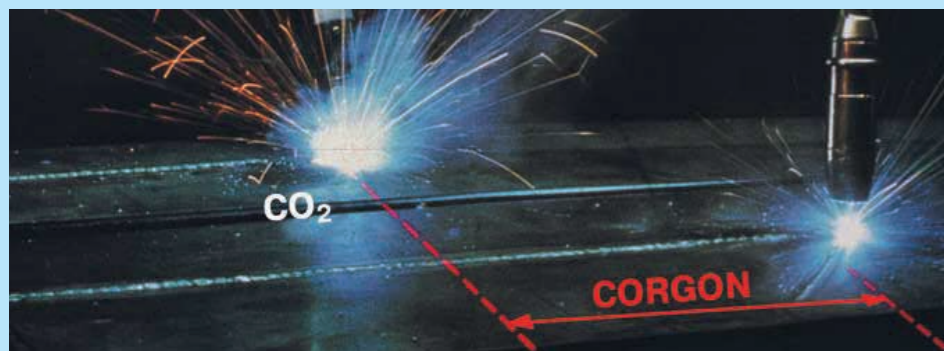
Увеличение скорости сварки при использовании смесей CORGON®
